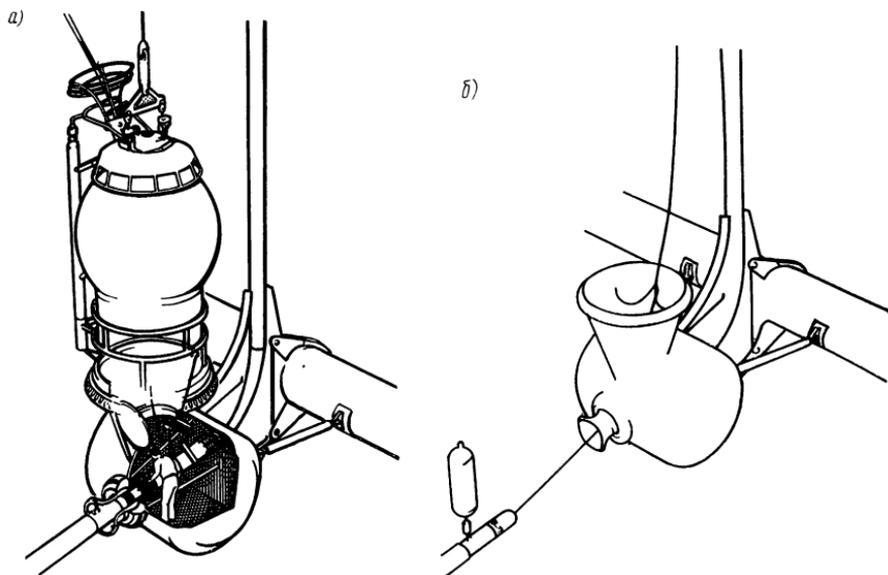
Сварочная система фирмы «Локхид петролеум сервис»: а — транспортный блок состыкован со сварочной камерой; б — сварочная камера.
